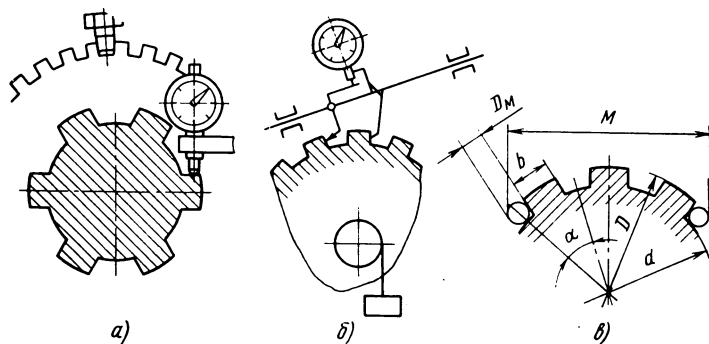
Схемы измерения погрешности окружного шага зубьев шлицевого вала:
